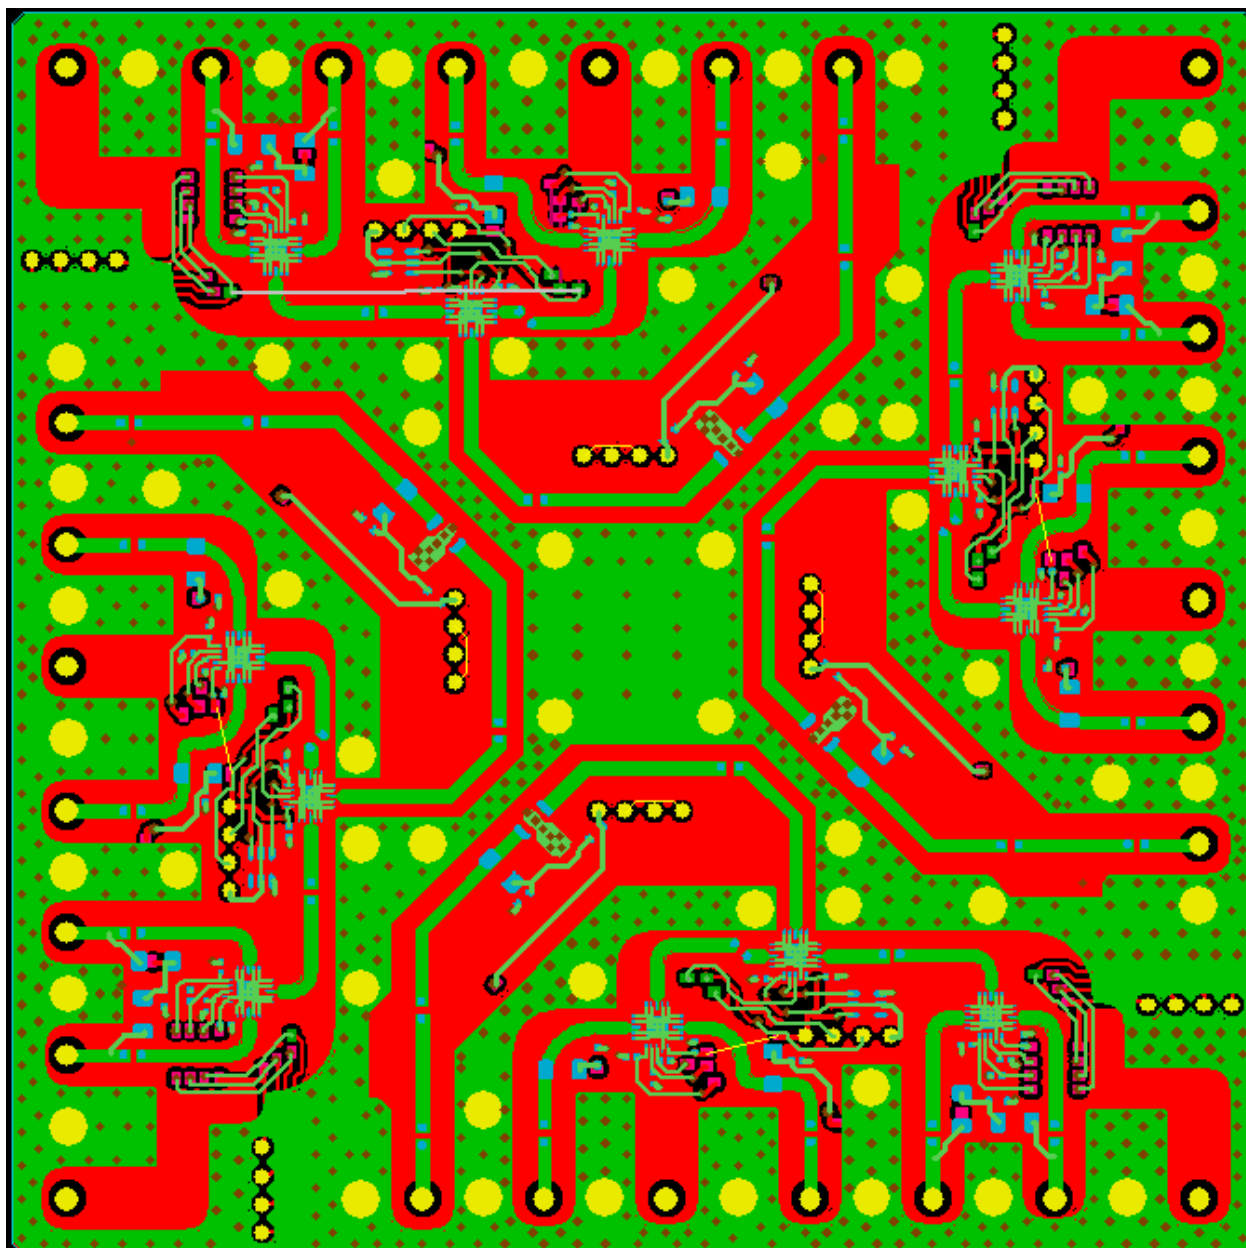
Верхній шар друкованої плати ВЧ комутатора
